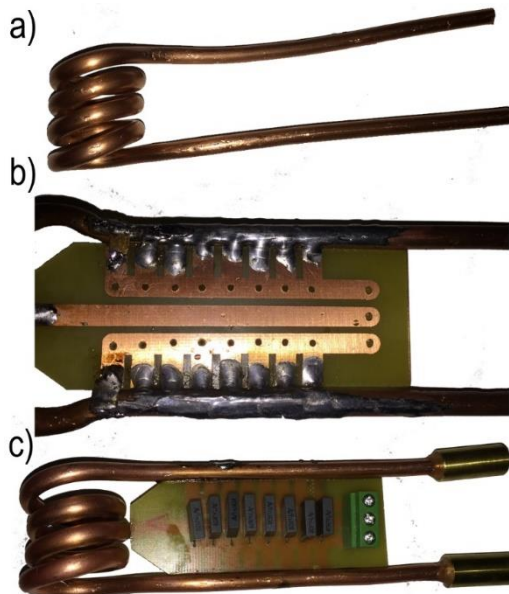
Construcción de las bobinas. a) Corte y doblez del tubo flexible de cobre para formar la bobina. b) Armado y soldado de la placa sobre la que se monta el arreglo de capacitores. c) placa final con el arreglo de capacitores soldados a la bobina y con coples para adaptar la bobina al sistema de enfriamiento.
